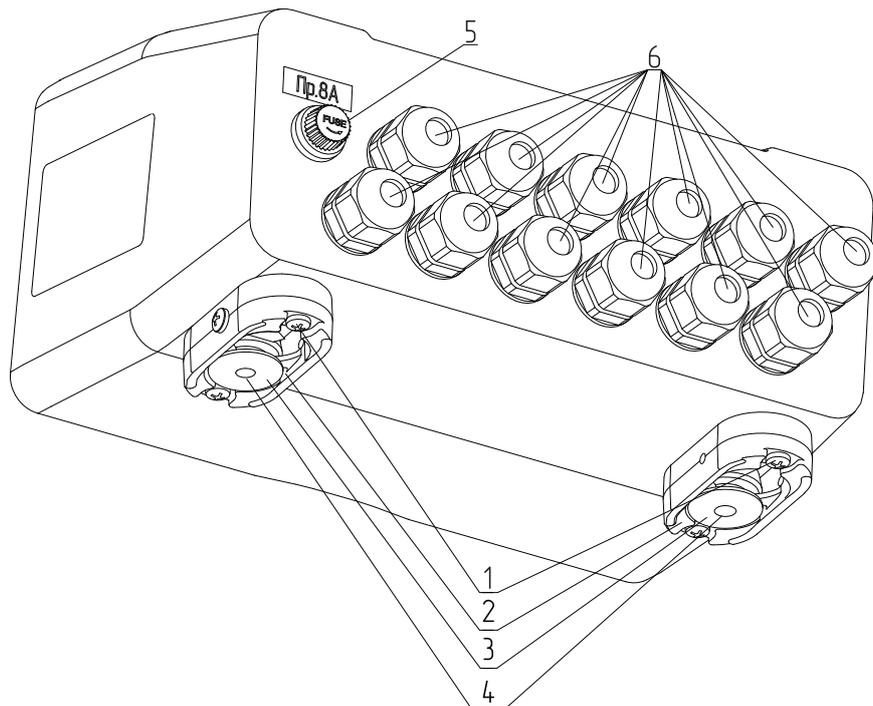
Внешний вид контроллера C-Line 200SF с фиксатором крепления
